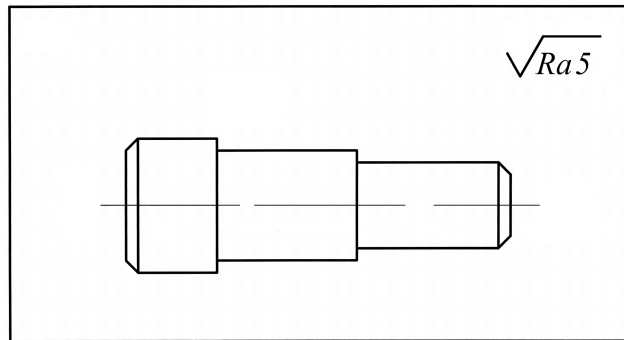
Обозначение шероховатости, когда все поверхности имеют одинаковую шероховатость
